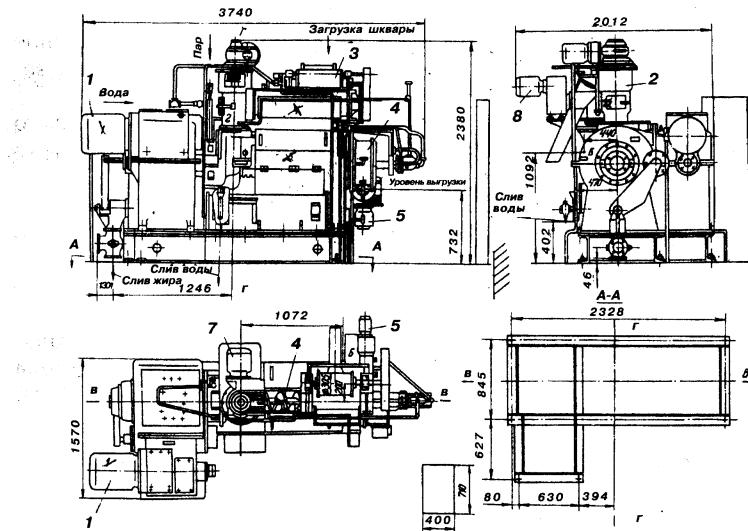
Габаритные и установочные размеры пресса Б6-ФОА:
